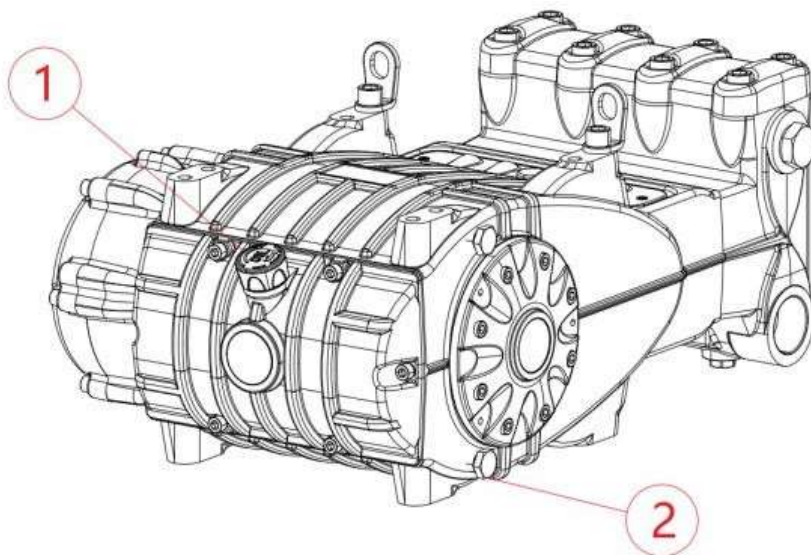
① — масляный щуп; ② — сливная пробка картера
